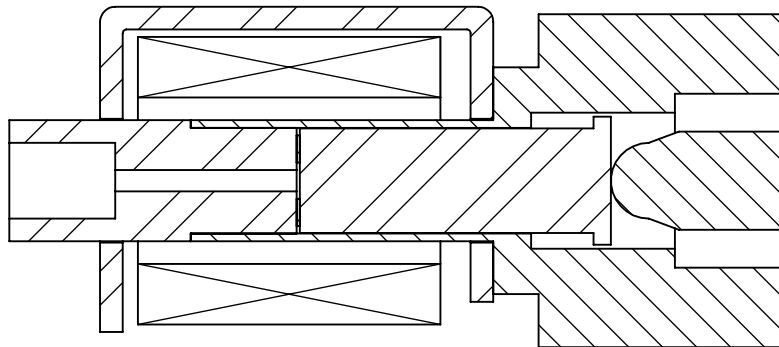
Magnetisch relevante Komponenten des Demonstratormagneten
